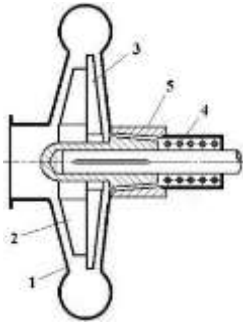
Схема безсальникового насоса: 1 – корпус; 2 – робоче колесо; 3 – додаткове колесо; 4 – пружина; 5 – втулка
